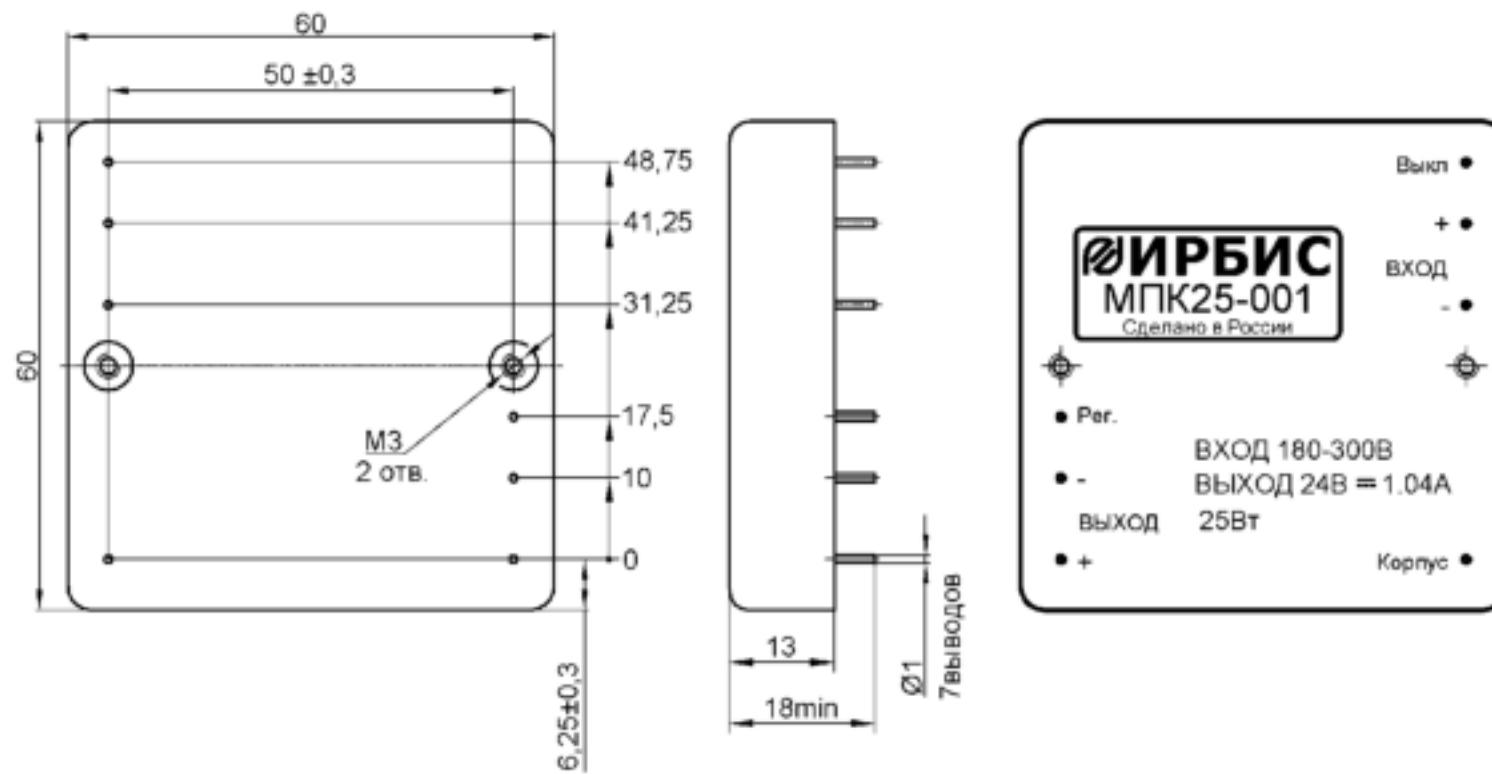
Габаритный чертеж модулей МПК25-001
